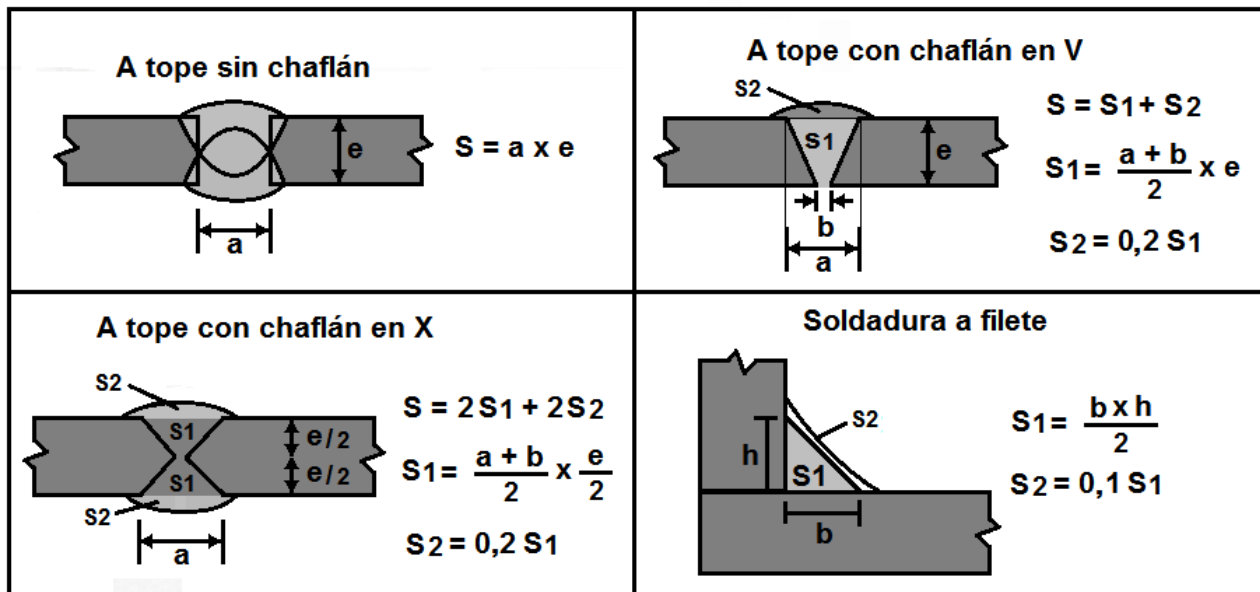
Cálculo de la sección de soldadura de acuerdo al chaflán o bisel (15)
